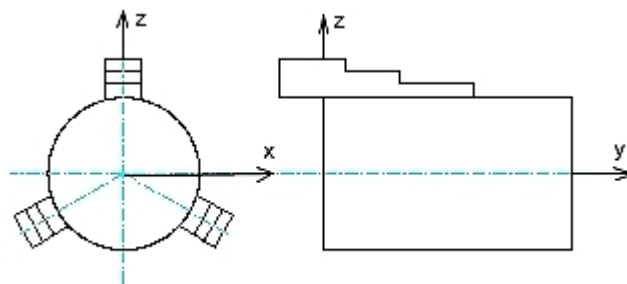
Установка вала в трехкулачковом самоцентруючому патроні.
